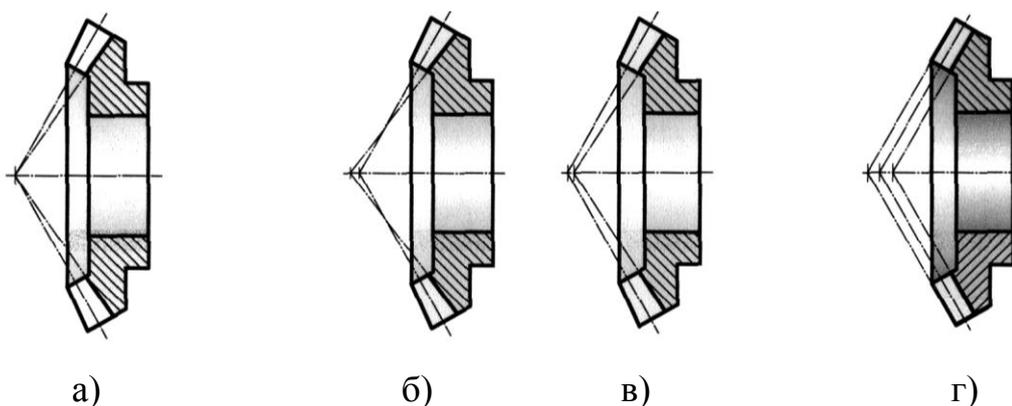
Осевая форма зубьев конических зубчатых колес
